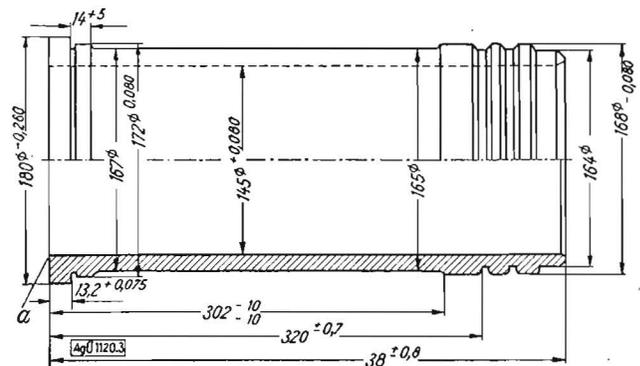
Buchse des Zylinderblocks vom Motor des Traktors S-80
